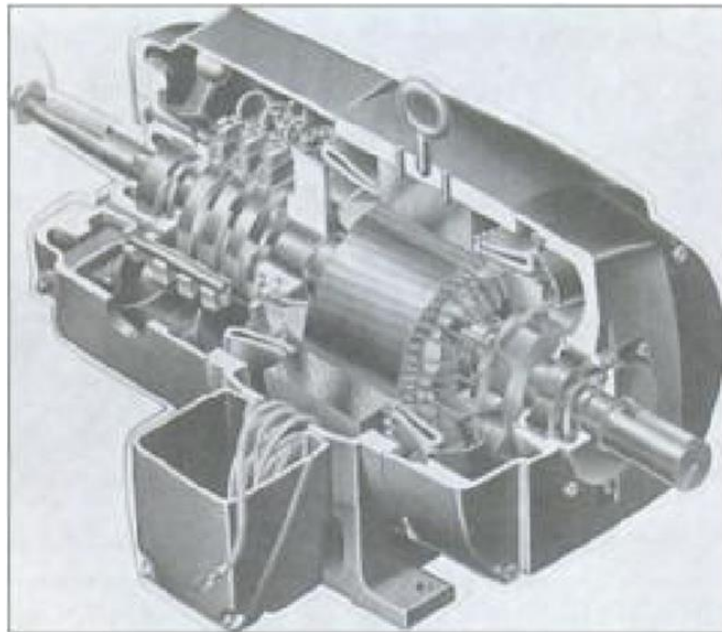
Vista em corte longitudinal de um motor de indução trifásico com um rotor bobinado.
